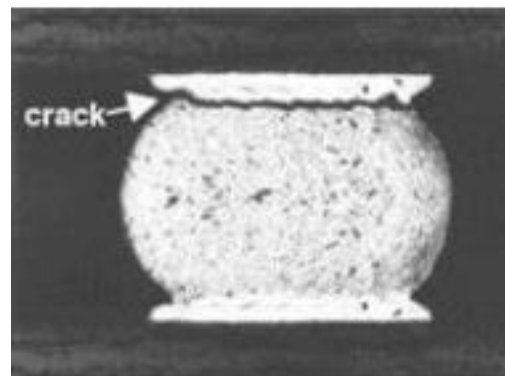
Connexion défaillante par fissuration de la patte
